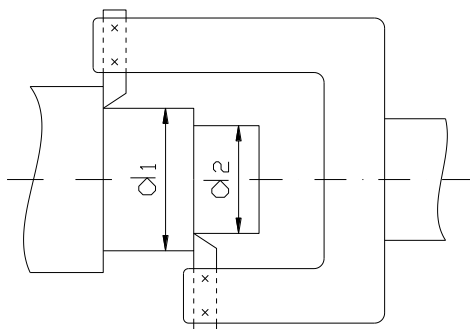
Одновременная обработка детали несколькими инструментами
